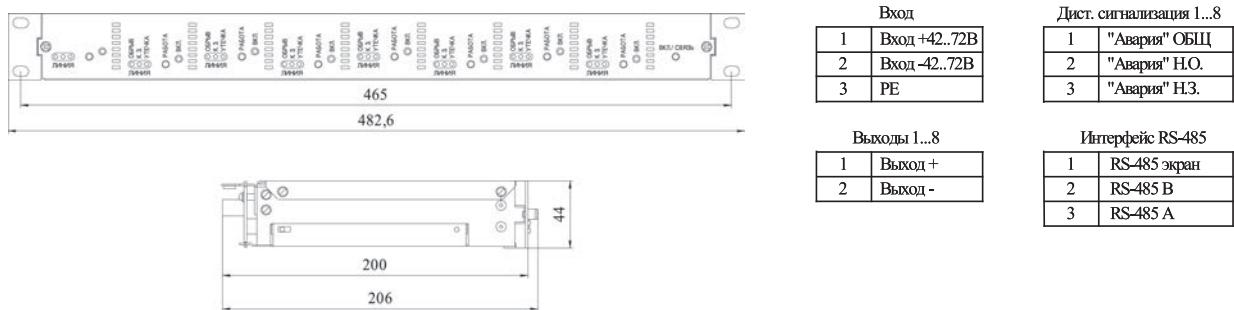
Габаритный чертеж УДЭП-280
